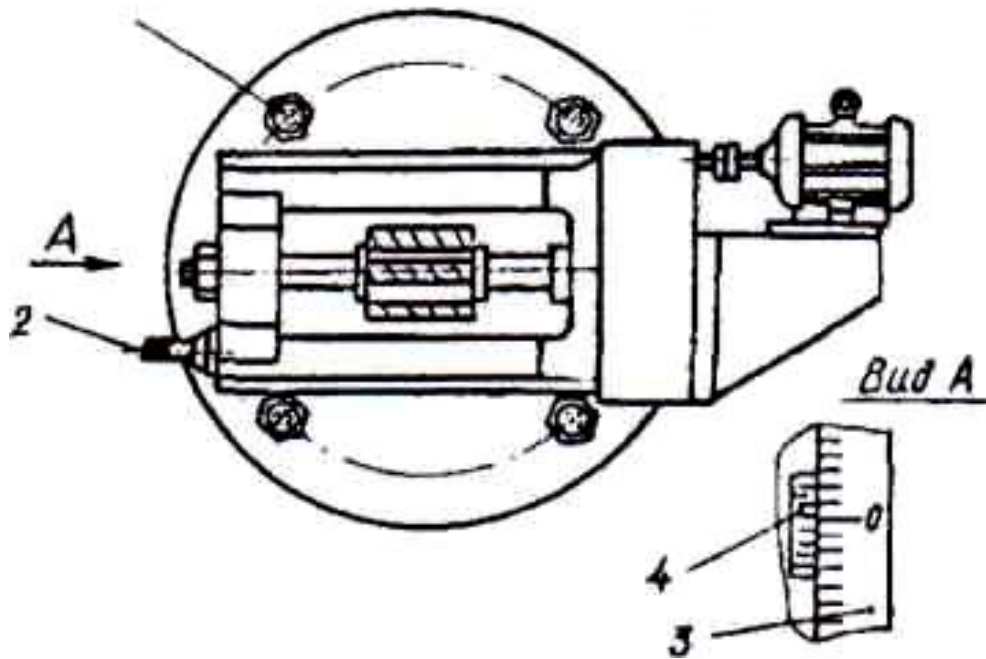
Схема установки фрезерного супорту на розрахований кут
